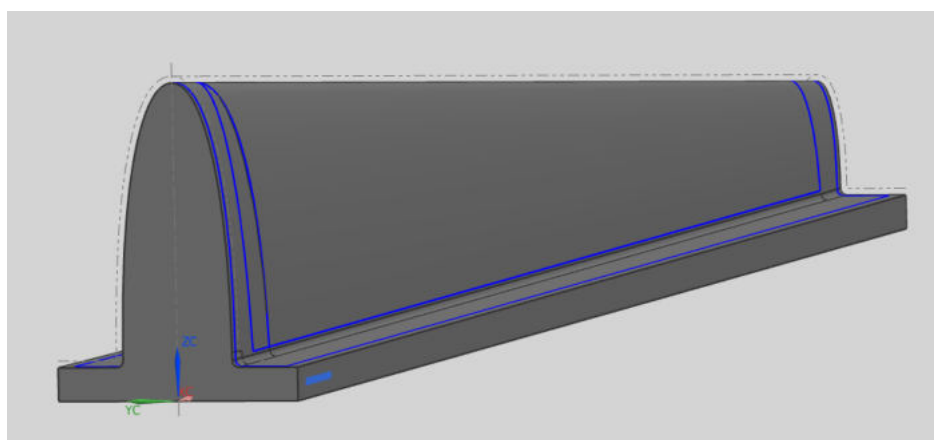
Мастер-модель для изготовления матрицы
